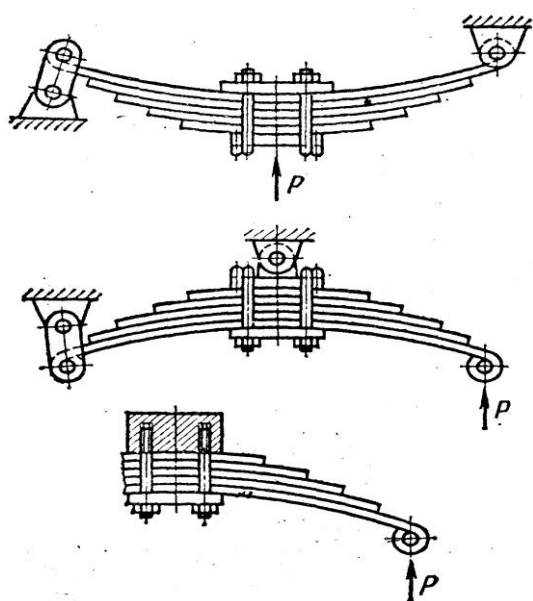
Варианты конструктивного исполнения металлических рессор с равным сопротивлением изгибу
